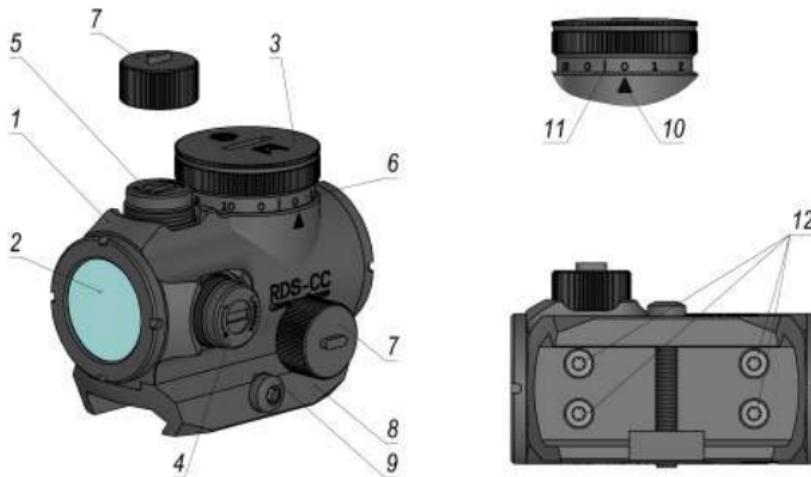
Устройство прицела коллиматорного RDS-CC
